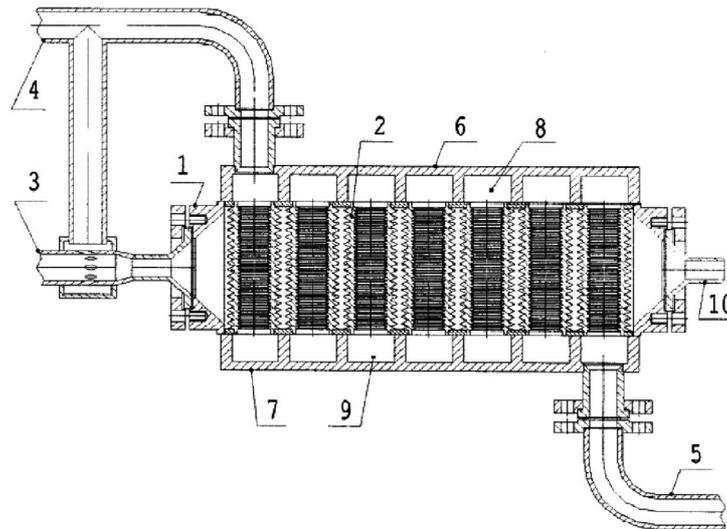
Смеситель-подогреватель для получения ВМЭ [3]:
